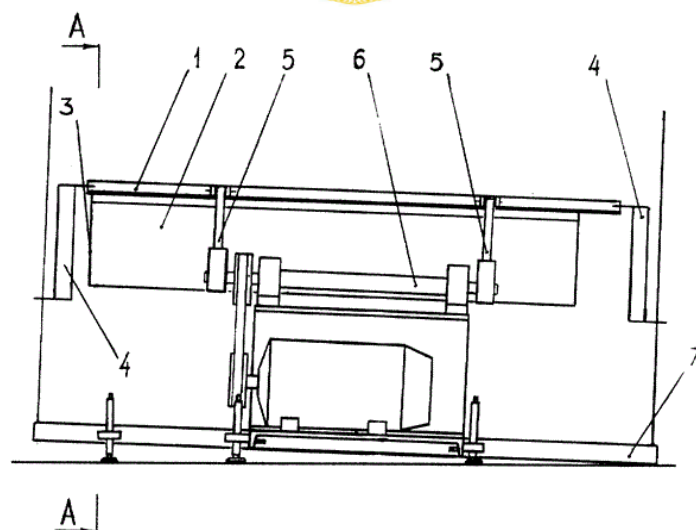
Вибрационный смеситель №3. Общий вид: 1,7 — рама; 2 — желоб цилиндрический; 3 — торцевая стена; 4 — рессоры; 5 — шатуны; 6 — вибровозбудитель
